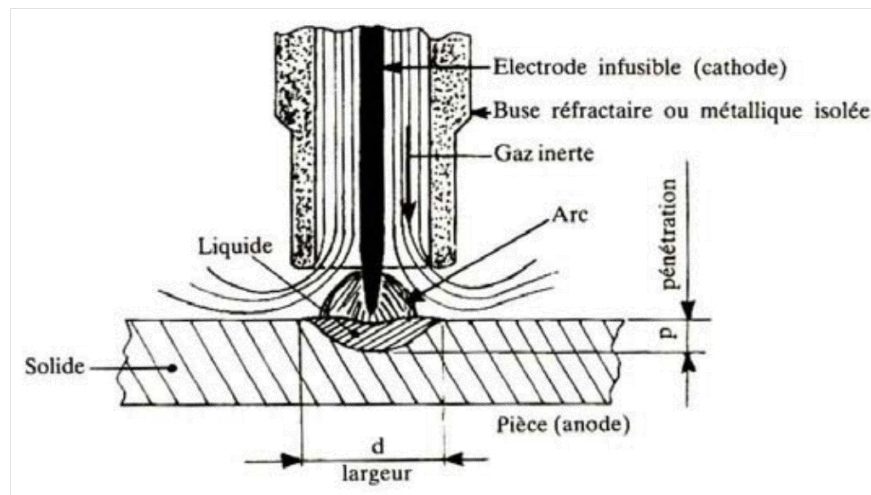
Principe du procédé de soudage TIG simple flux [5]
